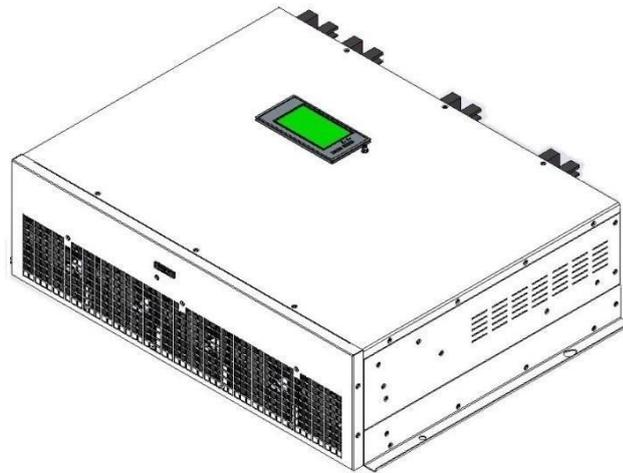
Módulo de tipo montado en la pared de 680 mm de ancho
